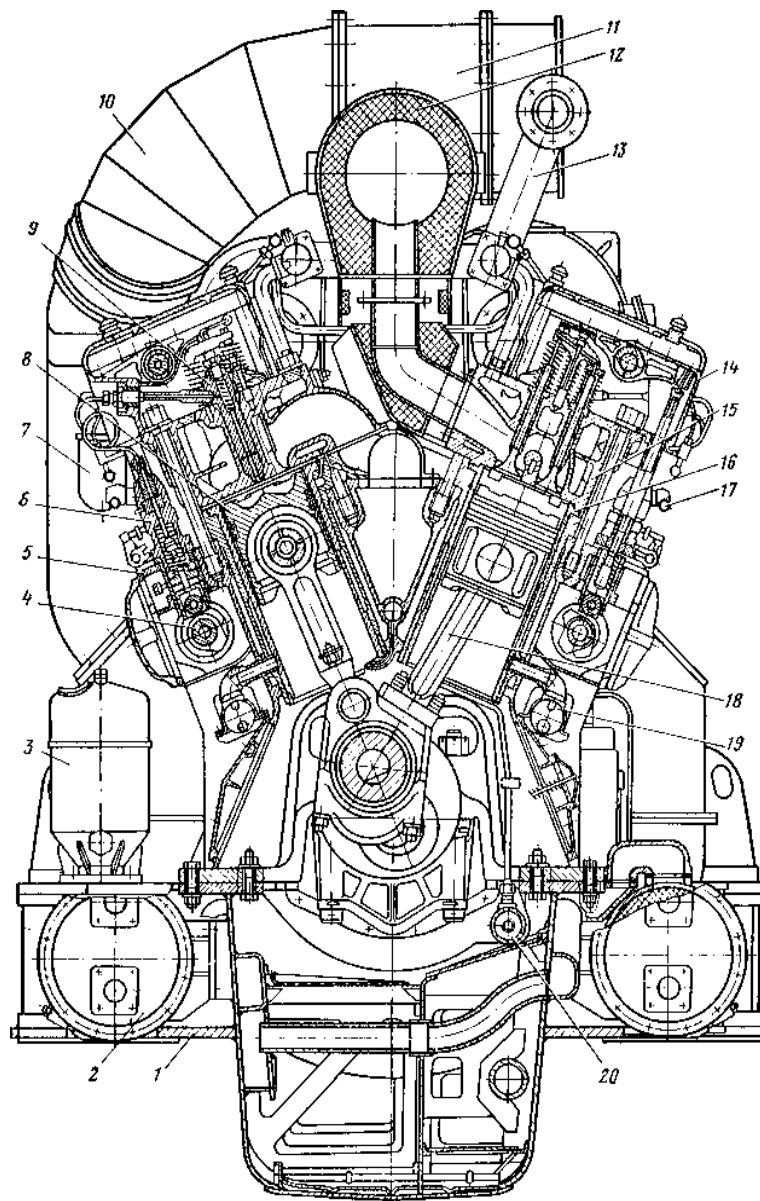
Поперечний переріз дизельного двигуна 2Д70
